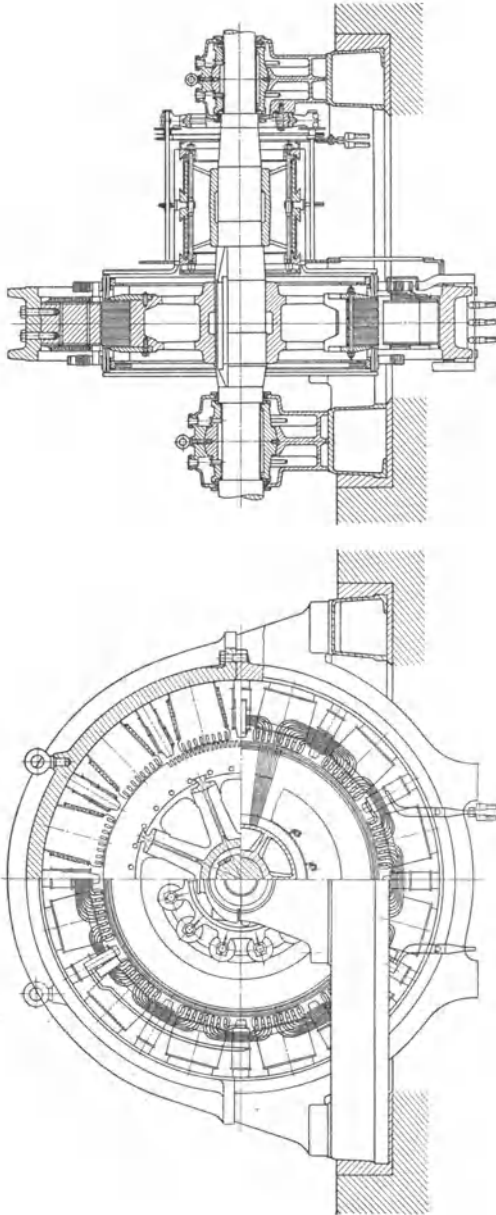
Gleichstrommaschine GM 600/30 der Siemens-Schuckertwerke, A.-G., Berlin. $N = 2400$ kW; 600 Volt, 4000 Amp. 593 U/min. Maßstab etwa 1:50. Großer, schnelllaufender Generator, wie er für Motorgeneratoren und für Leonard-Generatoren (Betrieb von Walzenstraßen und Fördermaschinen) Anwendung findet. Joch besteht aus Stahlguß, Hauptpole und Wendepole aus Dynamoblech. Kompensationswicklung, Kommutator zweiteilig.
